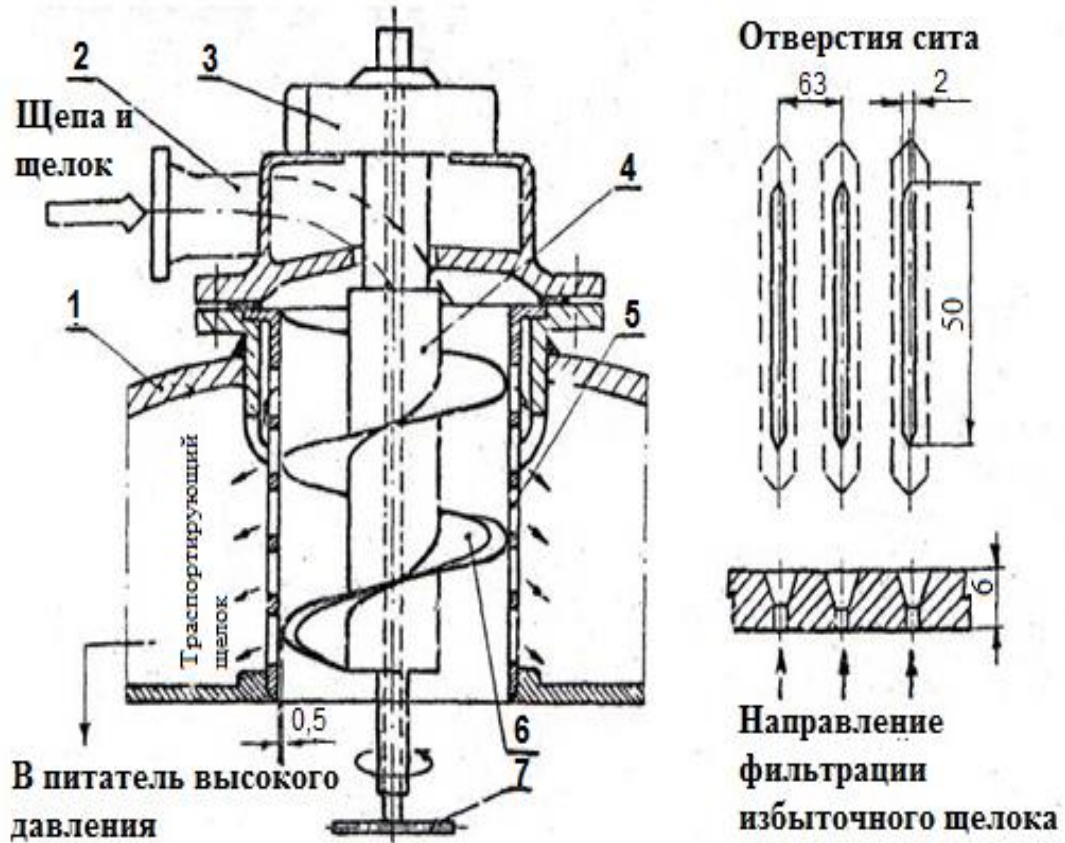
Загрузочное устройство варочного котла установки «Камюр»: 1-верхняя крышка котла «Камюр»; 2-патрубок для подачи щепы и щелока в котел из питателя высокого давления; 3-редуктор привода шнека; 4-шнек; 5-сито; 6-последний виток шнека удвоенной толщины; 7-датчик уровня щепы в котле
